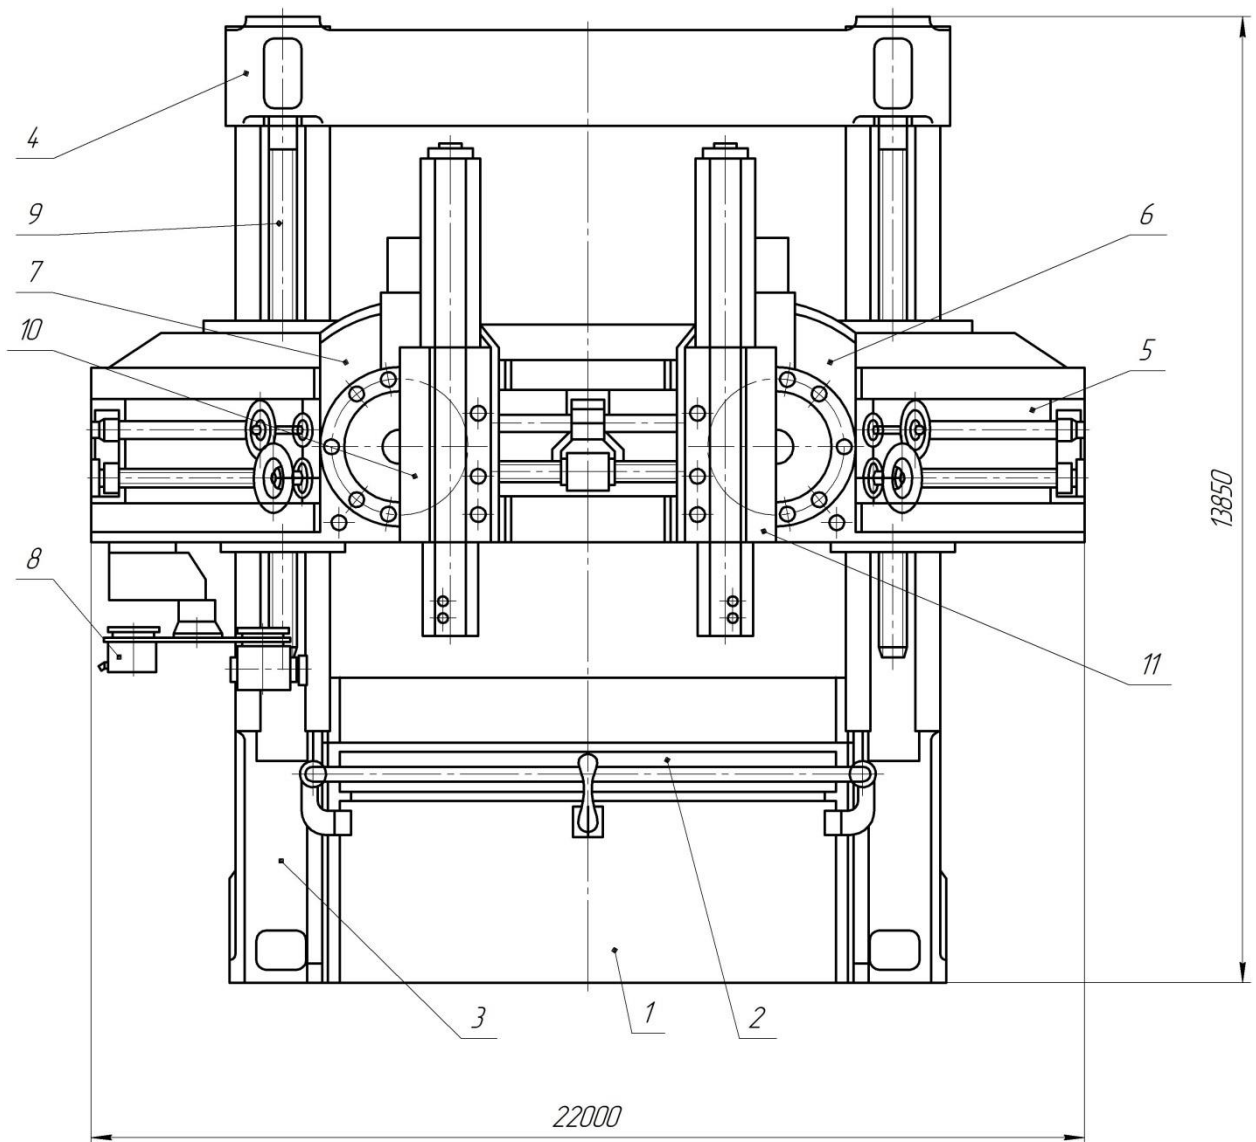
Загальний вид базової моделі верстата 1A563
